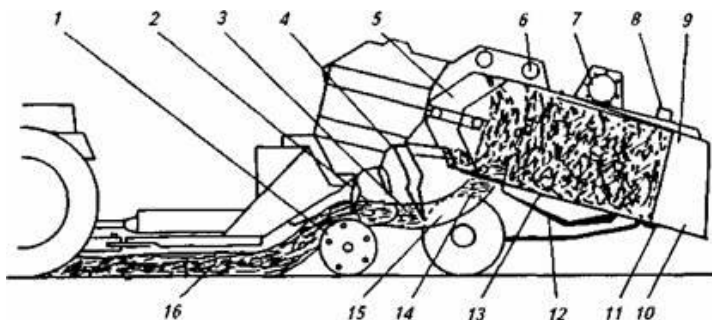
Схема рабочего процесса пресс-подборщика ПКТ-Ф-2:
